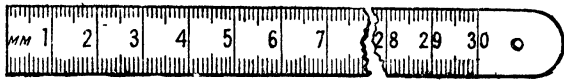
Разметочный и контрольно-измерительный инструмент:
